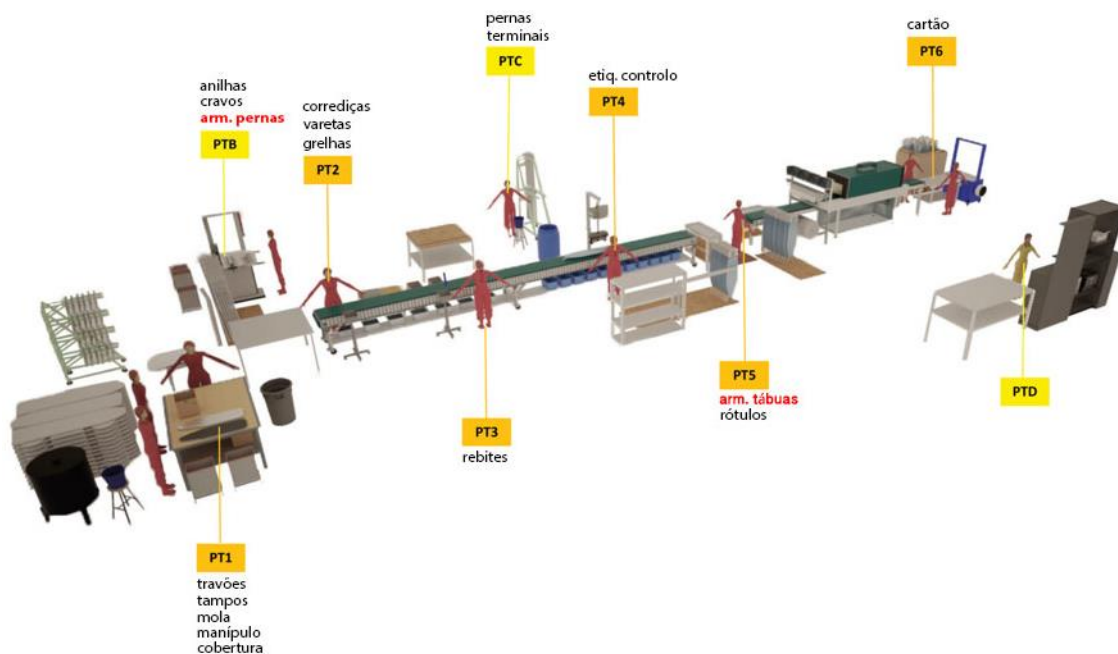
Ficha de Layout Linha 2 - ANEXO K
